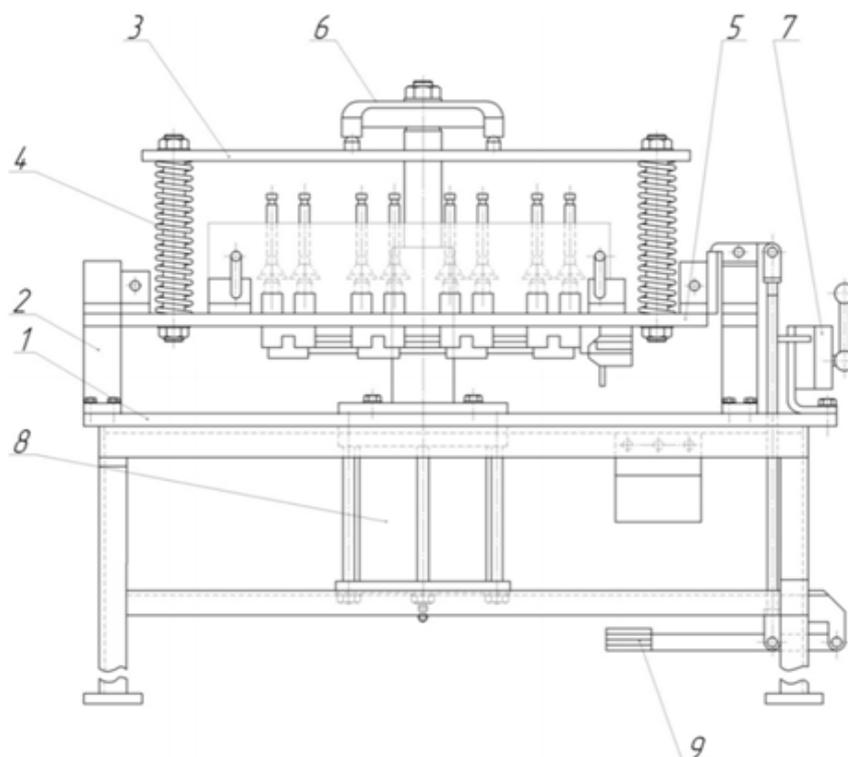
Приспособление для разборки и сборки головок блока цилиндров дизельных двигателей, где 1 – стол; 2 – стойка; 3 – планка нажимная; 4 – колонка; 5 – плита поворотная; 7 – кран пневматический; 6 – прижим; 8 – цилиндр пневматический; 9 – пневмоколлектор
